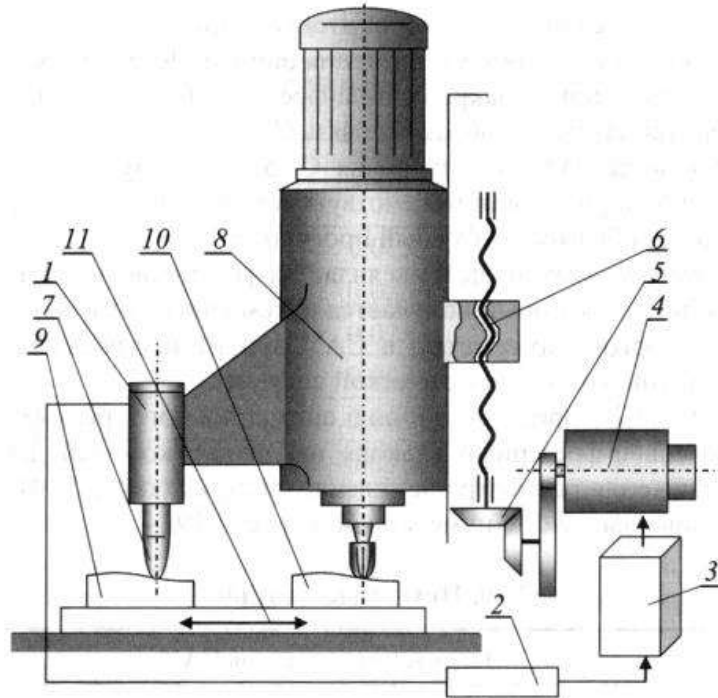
Принципова схема роботи копіювально-фрезерного верстата
